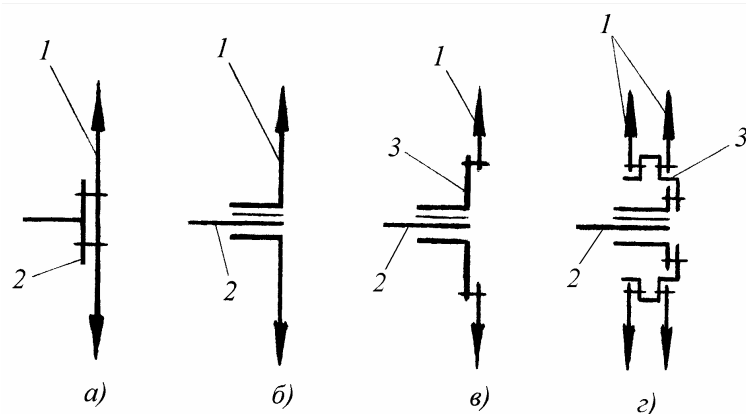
Конструктивные схемы ведущих колес гусеничного трактора: 1- зубчатый венец; 2 – ведомый вал конечной передачи; 3 – ступица
